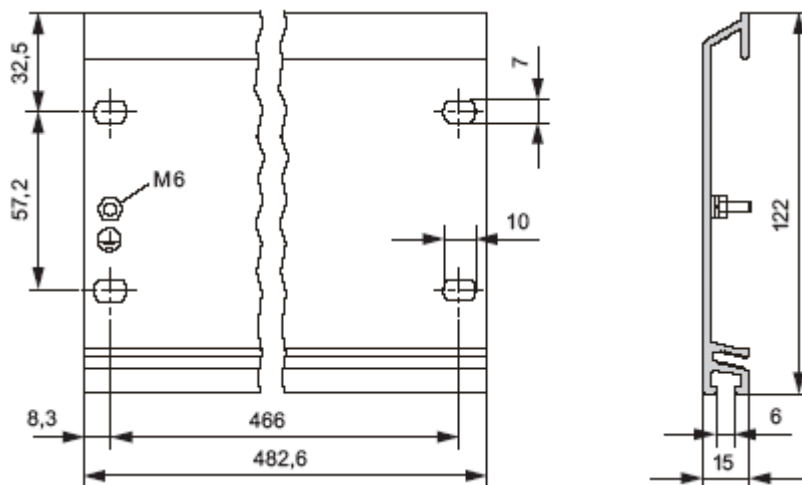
Габаритный чертеж профильной шины стандартной ширины 482,6 мм.
